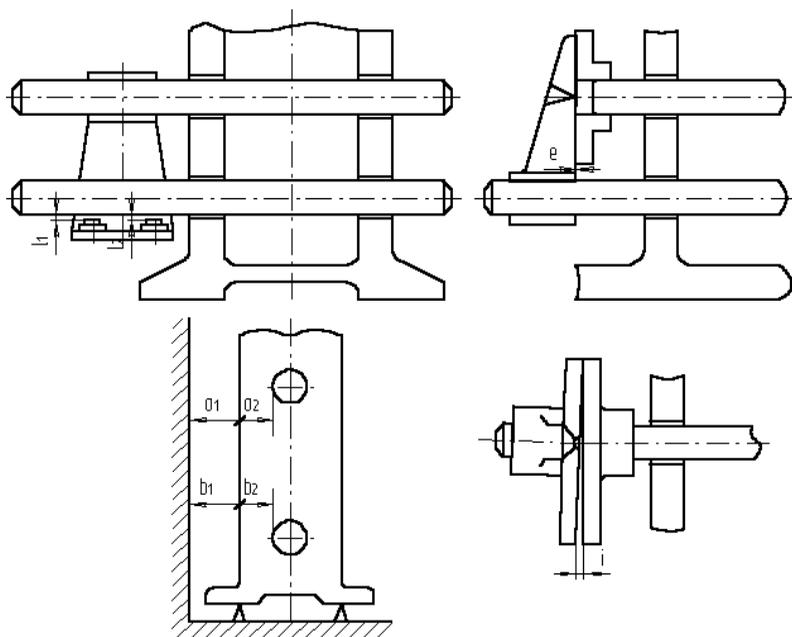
Схемы контроля параллельности и перекоса осей в корпусе зубчатых передач
